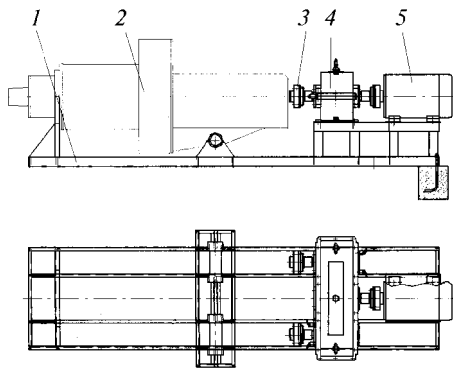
Стенд для обкатки редуктора привода фрез проходческого комбайна ПК-8
